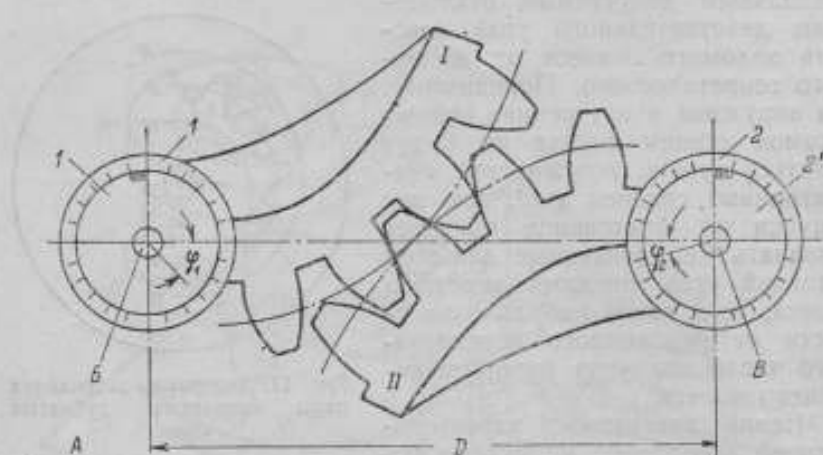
Схема простейшего приспособления для проверки зацепления некруглых зубчатых колес.
